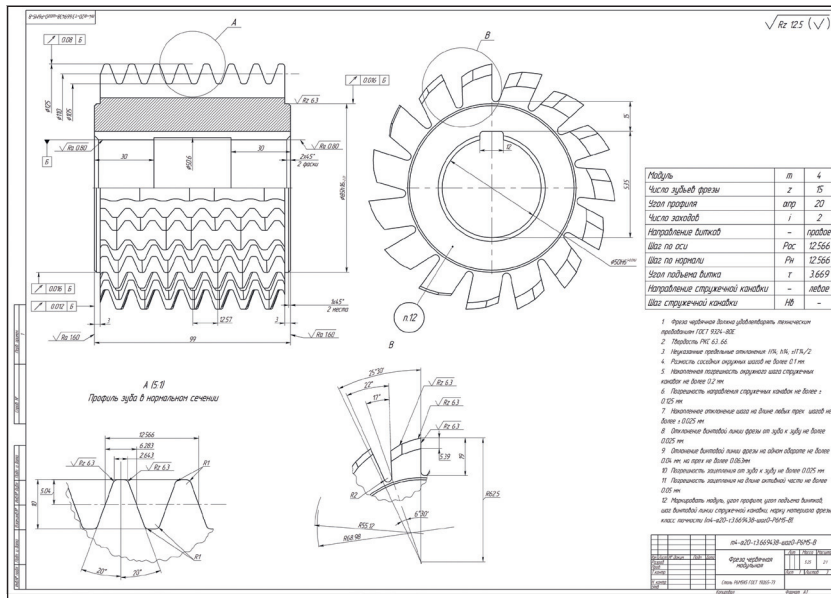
Исследование червячных зуборезных фрез для изготовления зубчатых колес
